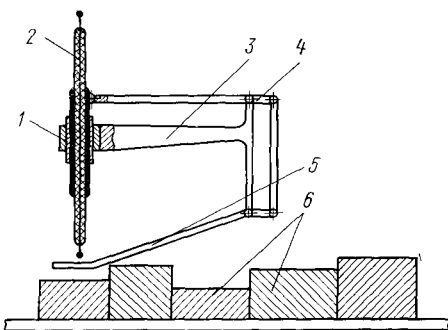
2 Приспособление для регулирования длины рабочего искрового промежутка в установках конвейерного типа
